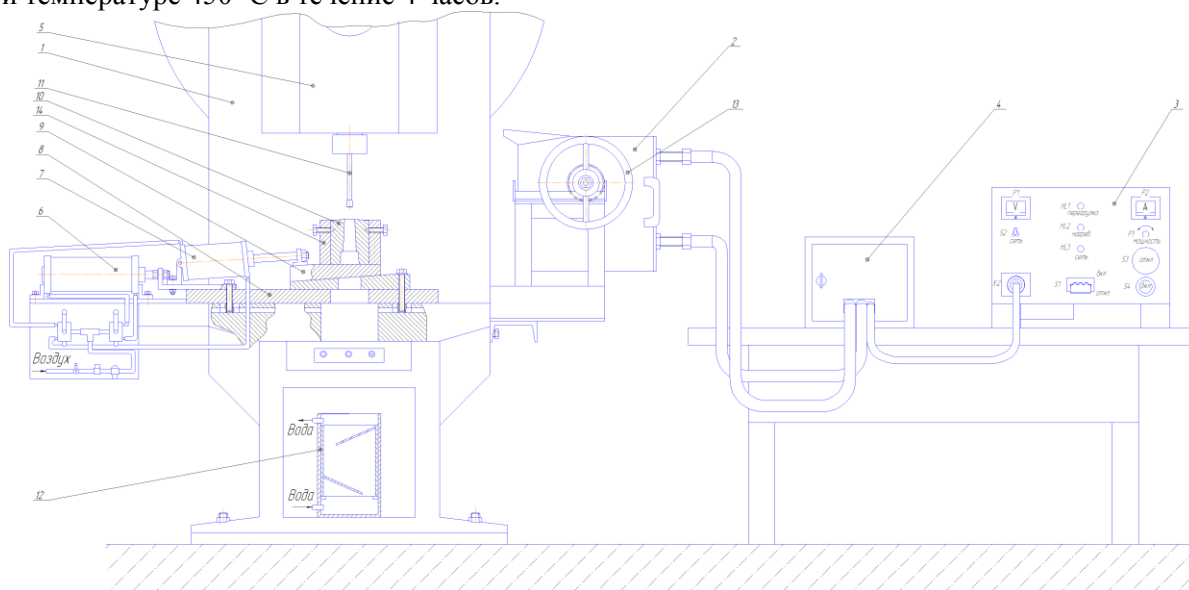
Установка для штамповки электродов контактной сварки
